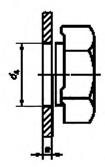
Присоединительные размеры (гайки еще не приварены)
